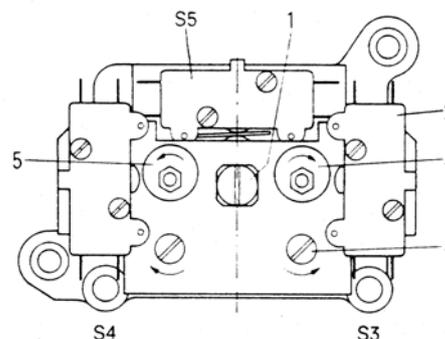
а: Роликовый контроллер (вид сверху)
